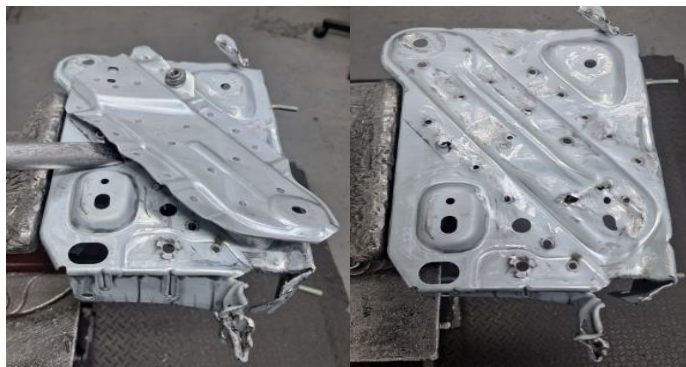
Teste de destaque dos pontos de solda (Fonte: autor)
